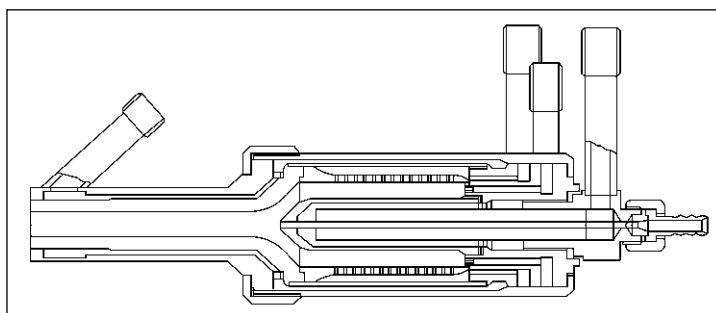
Схема прямооточной горелки для сверхзвукового газопламенного напыления
